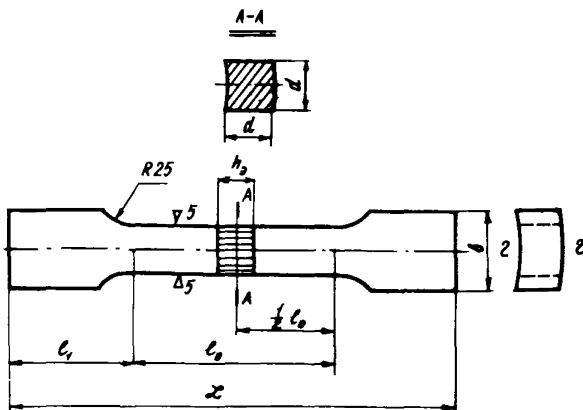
Чертеж образца с композитным швом для испытаний на разрыв
